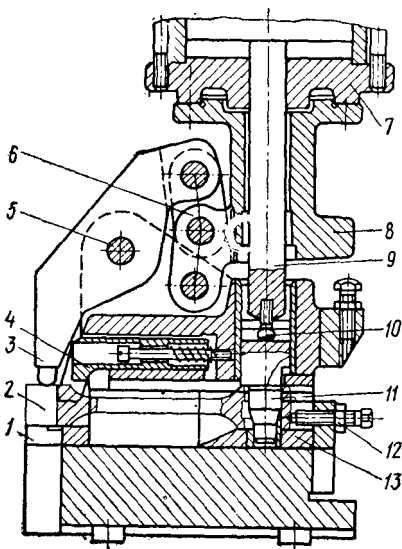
Приспособление к вертикально-протяжному станку для крепления рычагов при обработке плоскостей головки
